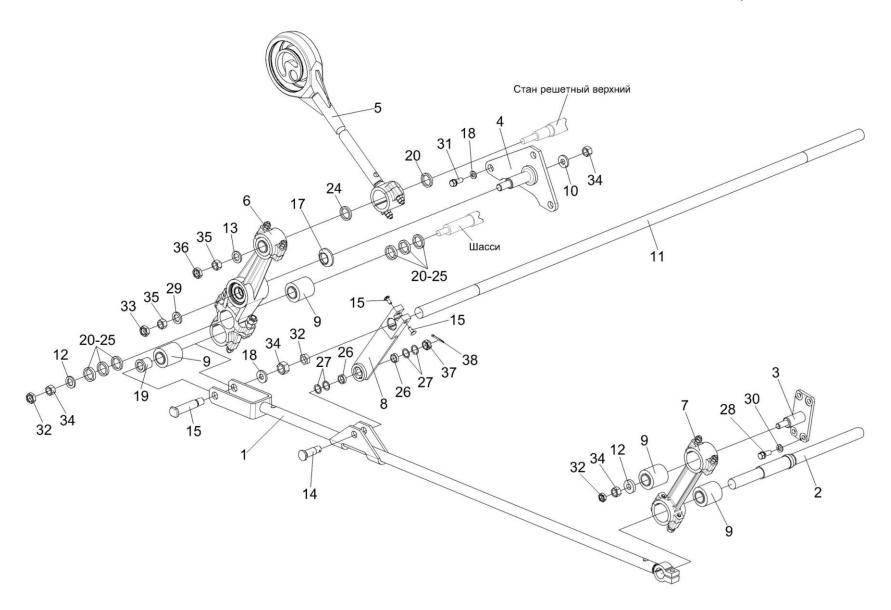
Установка привода доски стрясной КЗК 0280000А (вид справа)
